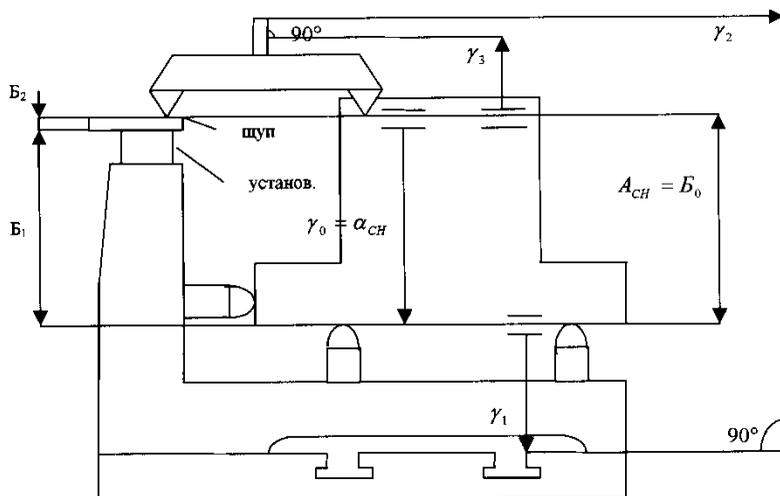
Размерные цепи статической настройки ТС вертикально-фрезерного станка
